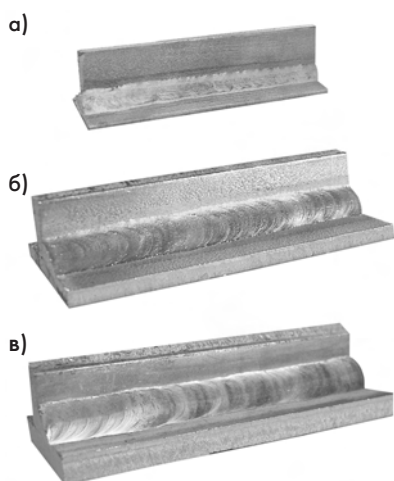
Внешний вид сварных тавровых соединений из сплава АМг-61 толщиной: а — (1,5+1,5) мм; б — (3+3) мм; в — (5+5) мм
